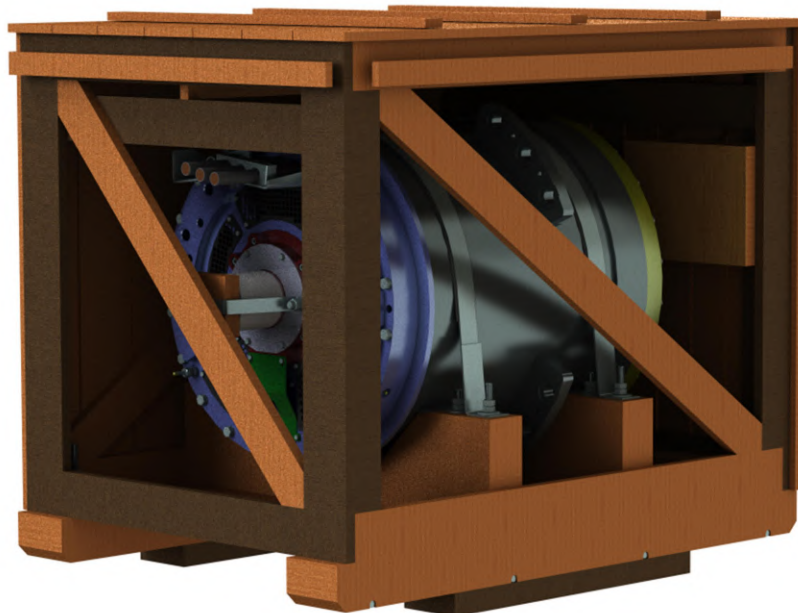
Упаковка двигателя АТД-4450/6 (стенки не показаны)
